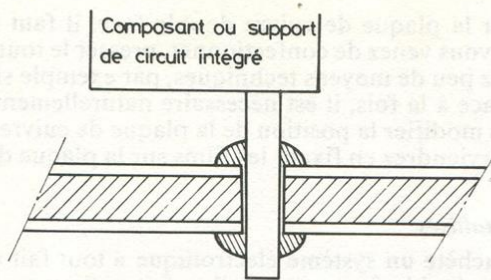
Soudage des composants sur les deux faces
